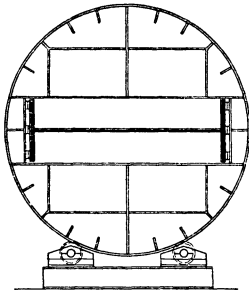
Drehvorrichtung zum Schweißen großer Bauteile.
